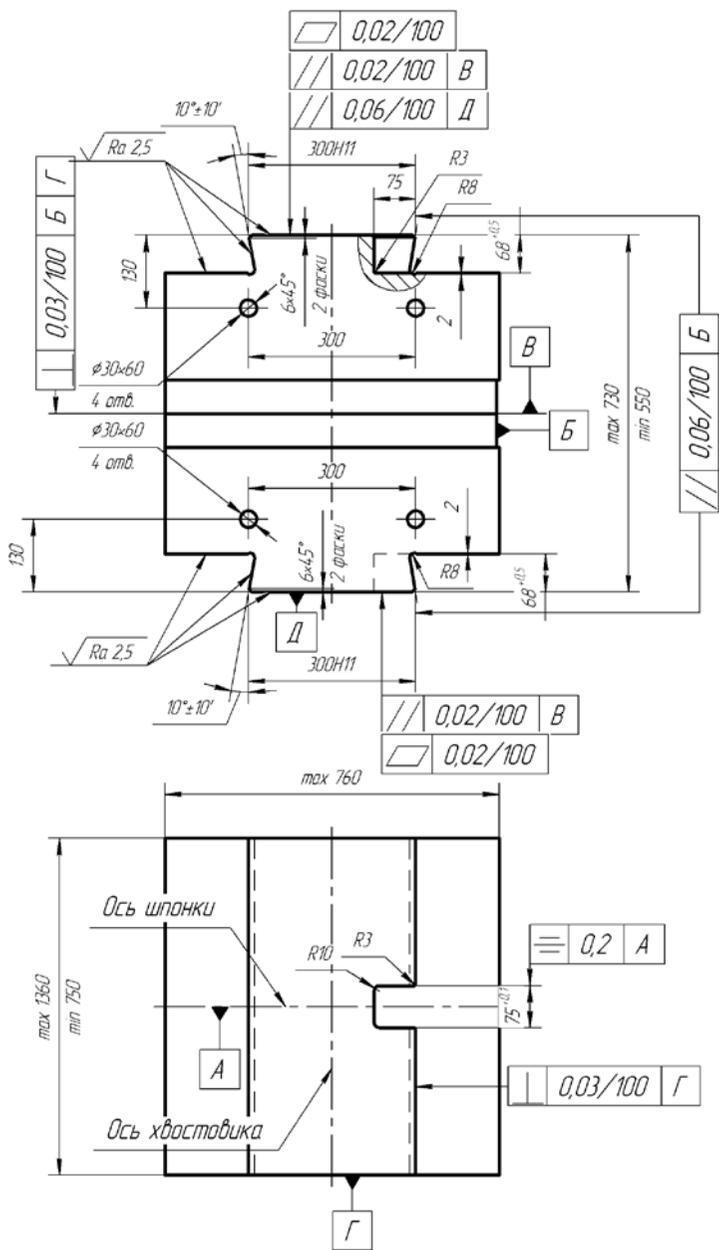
Габаритные и присоединительные размеры штампа для молота MA2147
